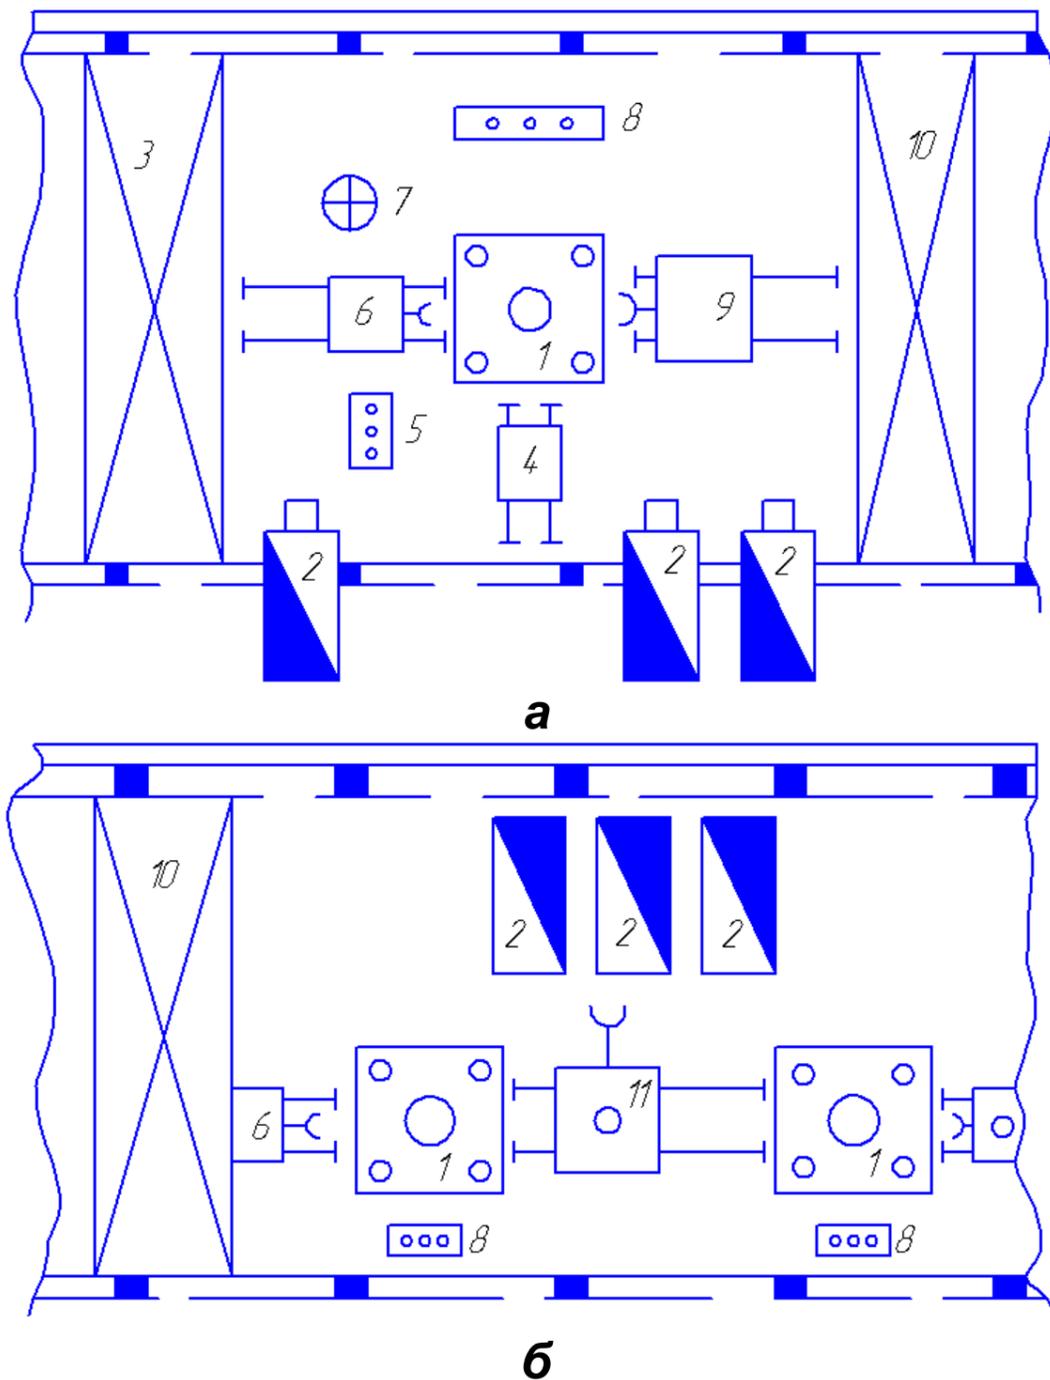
Схема расположения оборудования в агрегате ковочного гидравлического прессы усилием 20 МН (а) и прессов усилием 8–12,5 МН (б), обслуживаемых посадочными машинами:
